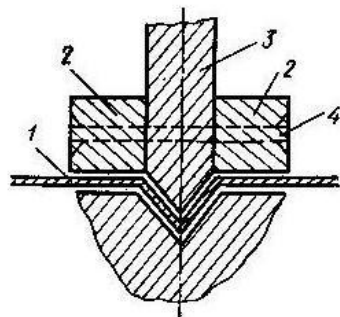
Приспособление для изготовления профилированных панелей на кромкогибочном станке:
